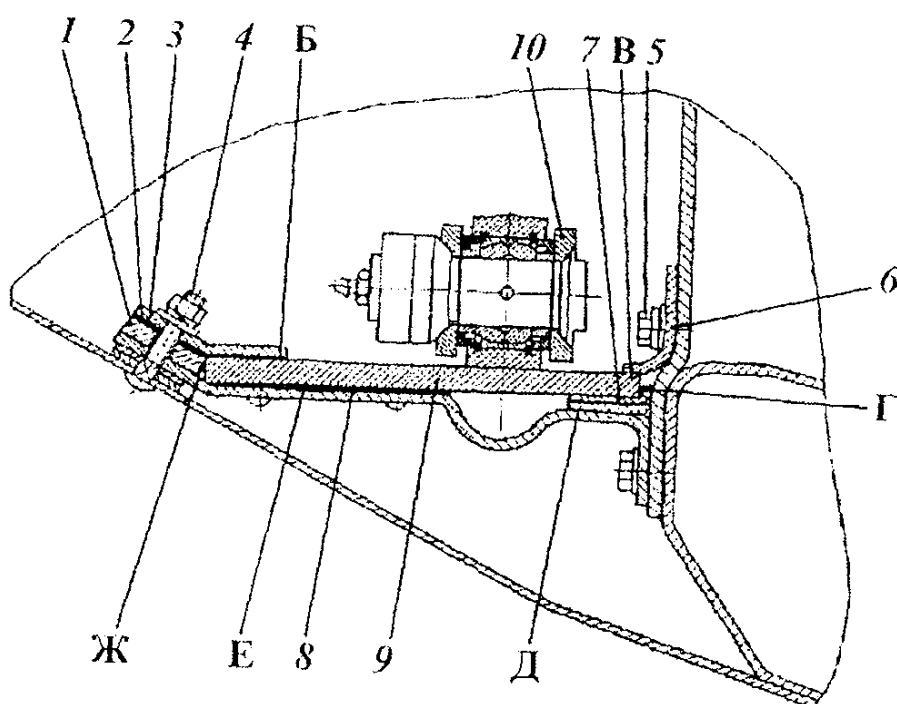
Соединение ножа с приводом: 1,7 – пластины трения; 2 – регулировочная прокладка; 3,6 – прижимы; 4,5 – болты; 8 – пластина; 9 – головка ножа; 10 – щетка; Б, В, Г, Д, Е и Ж – места контроля зазоров
